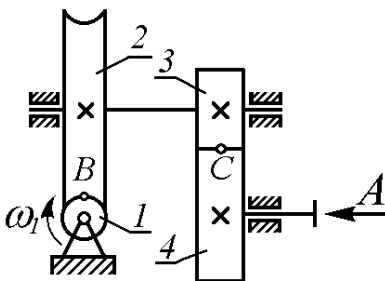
Двоступінчастий черв'ячно-циліндричний редуктор
